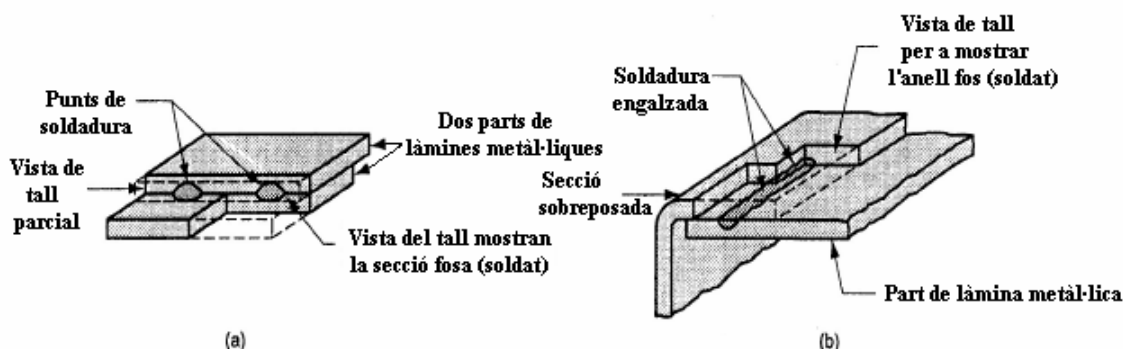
(a) Soldadura de punts i (b) soldadura engalzada
